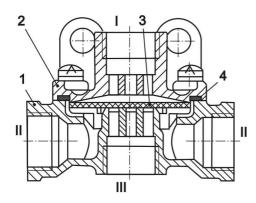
Клапан быстрого оттормаживания 1-корпус; 2- крышка; 3- диафрагма; 4- кольцо уплотнительное; I, II, III-выводы
